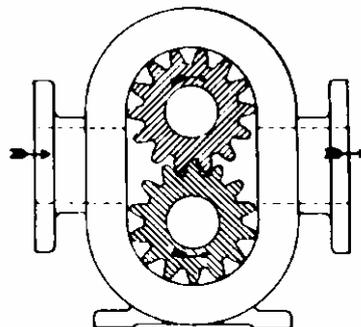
Corte de una bomba de engranajes rotativos.
